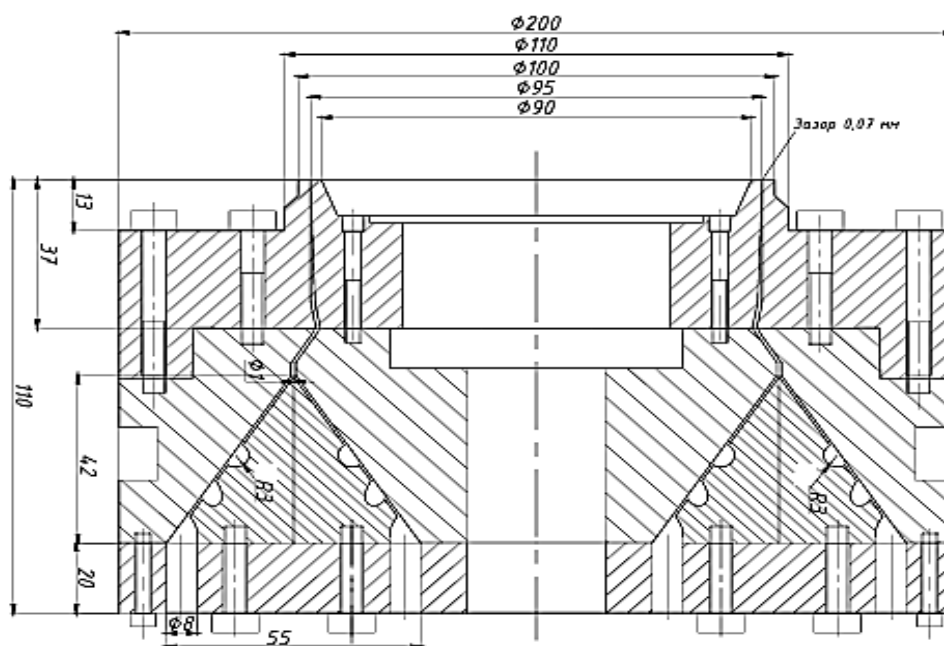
Креслення ко-екструзійної головки для виготовлення двошарової рукавної плівки
